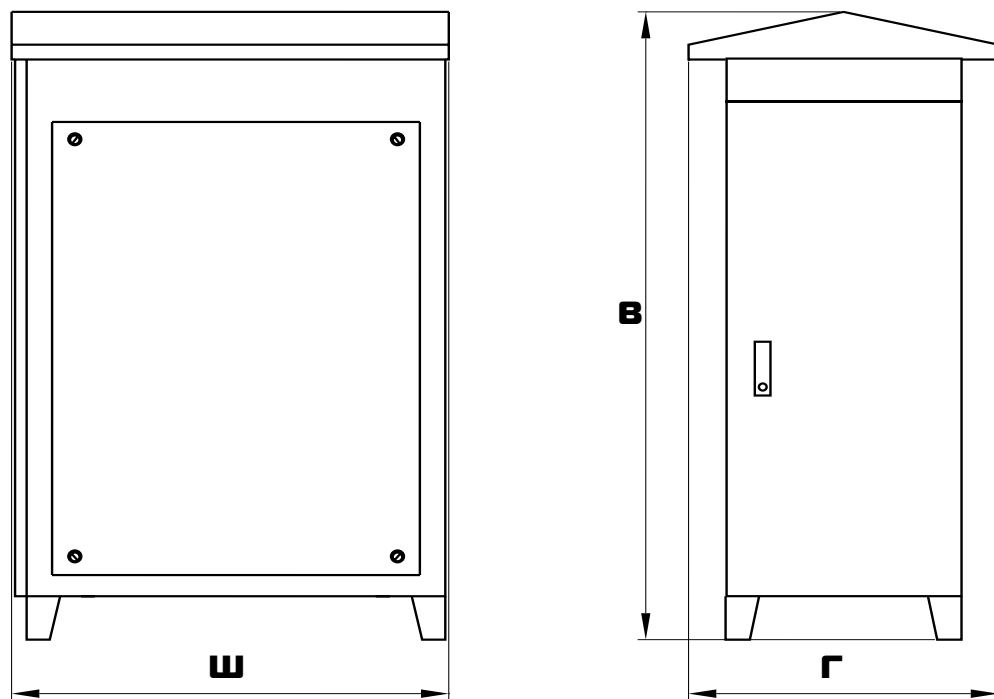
Габаритный чертеж трехфазного СТЭМ-2 IP20 300, 500 кВА
